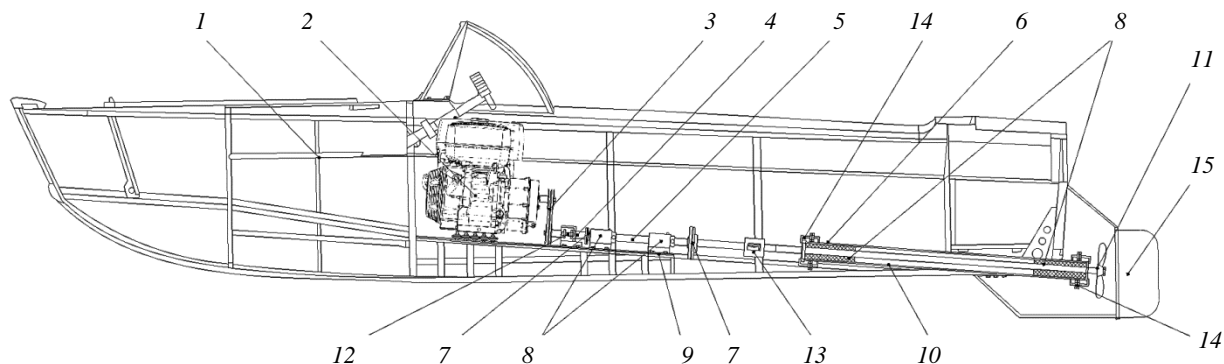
Конструкция экспериментального маломерного судна: 1 – корпус маломерного судна; 2 – поршневой ДВС; 3 – клиноременная передача; 4 – упорный вал; 5 – промежуточный вал; 6 – гребной вал; 7 – фланцевые соединения; 8 – подвижные опоры; 9 – фундамент; 10 – дейдвудная труба; 11 – гребной винт; 12 – упорный подшипник; 13 – измерительная тензометрическая аппаратура; 14 – уплотнения гребного вала; 15 – рулевое устройство
